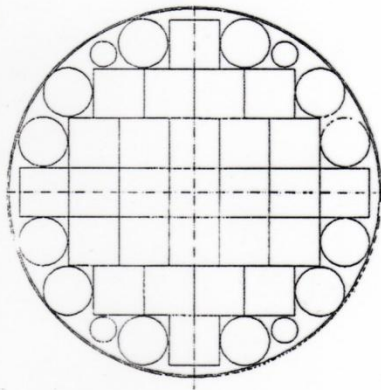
Схема раскроя крупногабаритной заготовки на отдельные режущие пластины различной формы.
